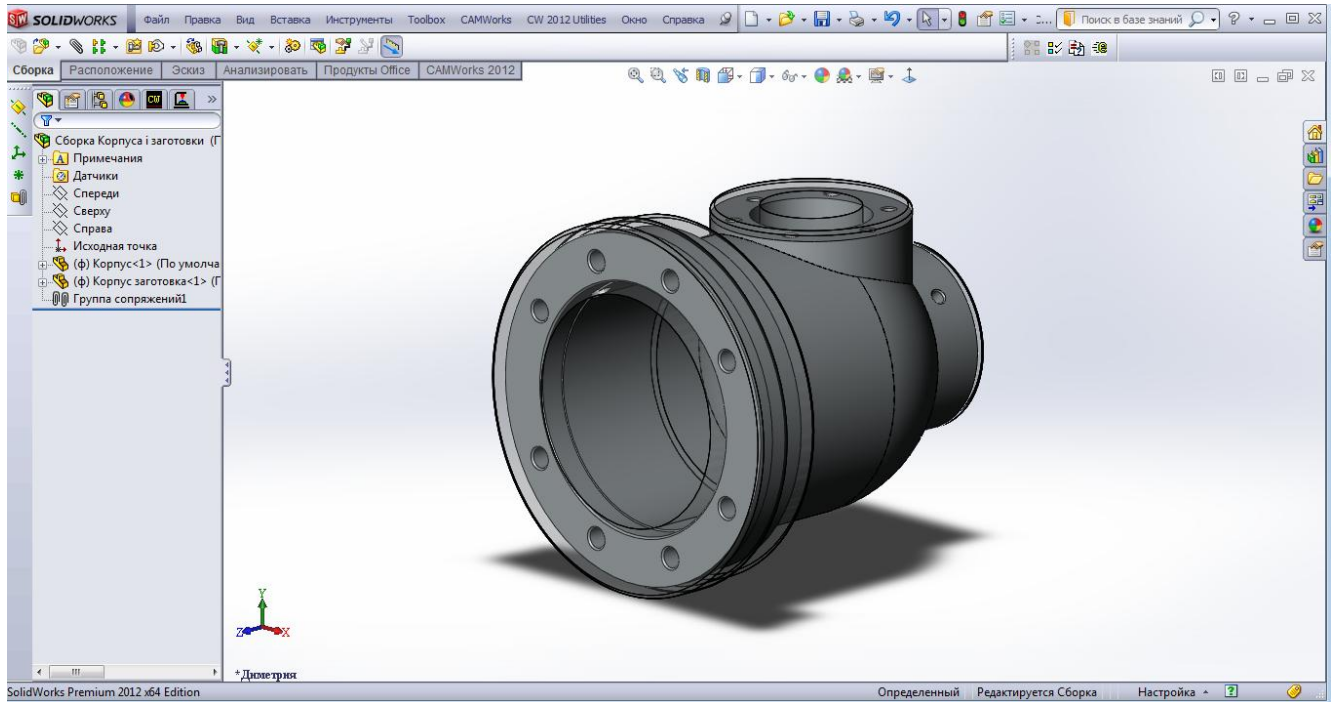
Зборка моделі «Корпус ДГК 10.030.20» з моделлю заготовки
